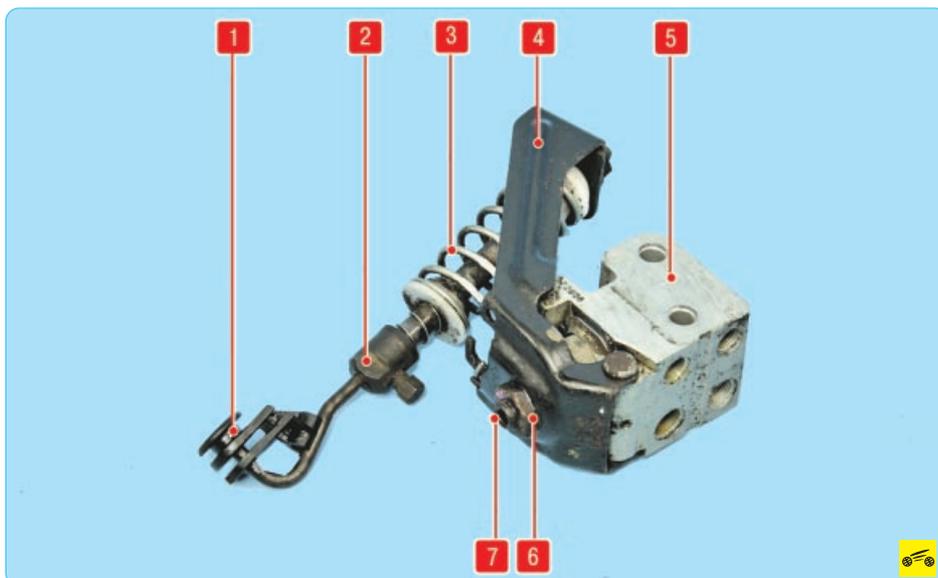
Регулятор давления в гидроприводе задних тормозов: 1 – фиксатор крепления нагрузочного стержня регулятора к балке задней подвески; 2 – нагрузочный стержень; 3 – нагрузочная пружина; 4 – рычаг; 5 – корпус регулятора давления; 6 – контргайка; 7 – регулировочный болт
